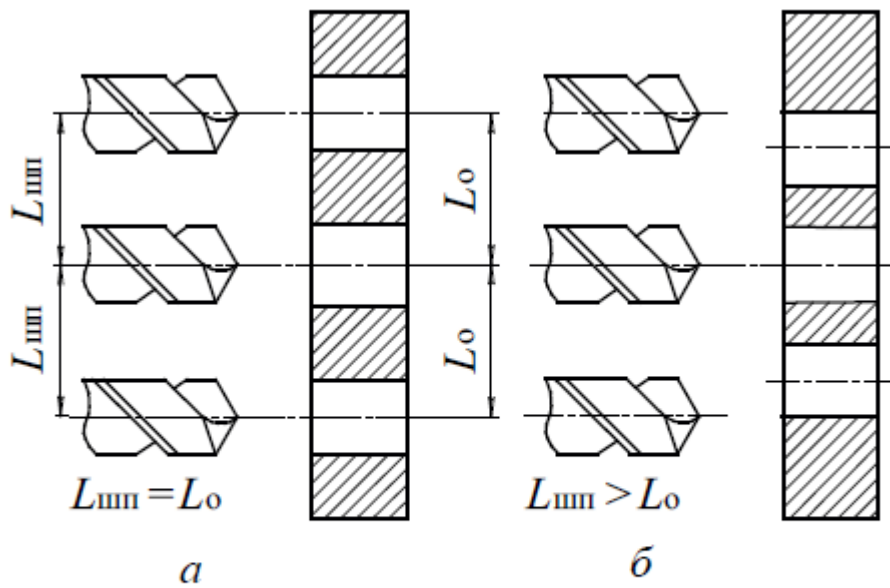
Конструкция корпусных деталей с отверстиями:
